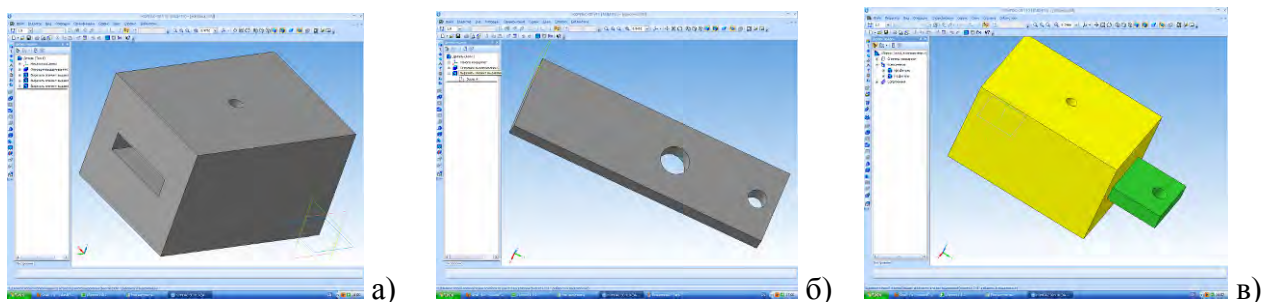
Приспособление для формования таблетированных брикетов с использованием программы КОМПАС -3D V10: а) корпус приспособления; б) планка (заслонка); в) приспособление в сборе
